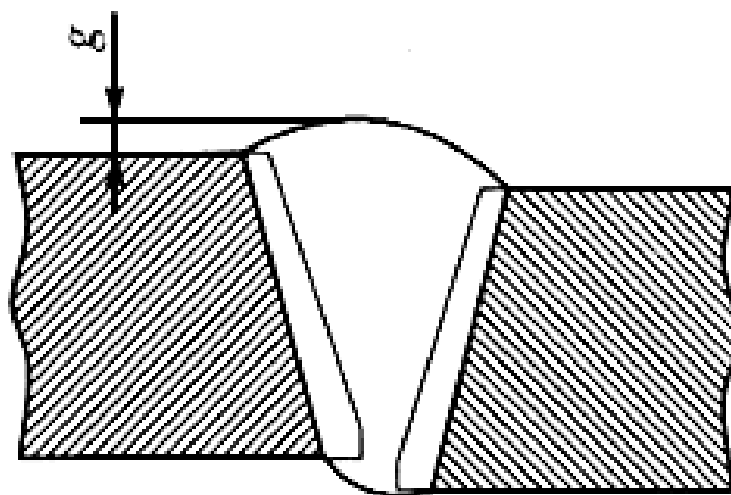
Измерение выпуклости (вогнутости) стыкового шва (g) при различном уровне наружных поверхностей деталей, вызванном смещением при сборке соединения под сварку
